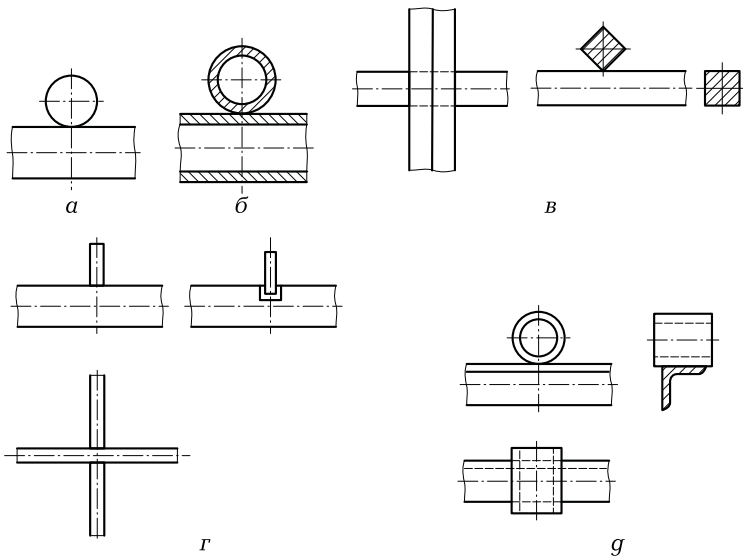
Типы рельефов при контактной рельефной сварке вкрест:
